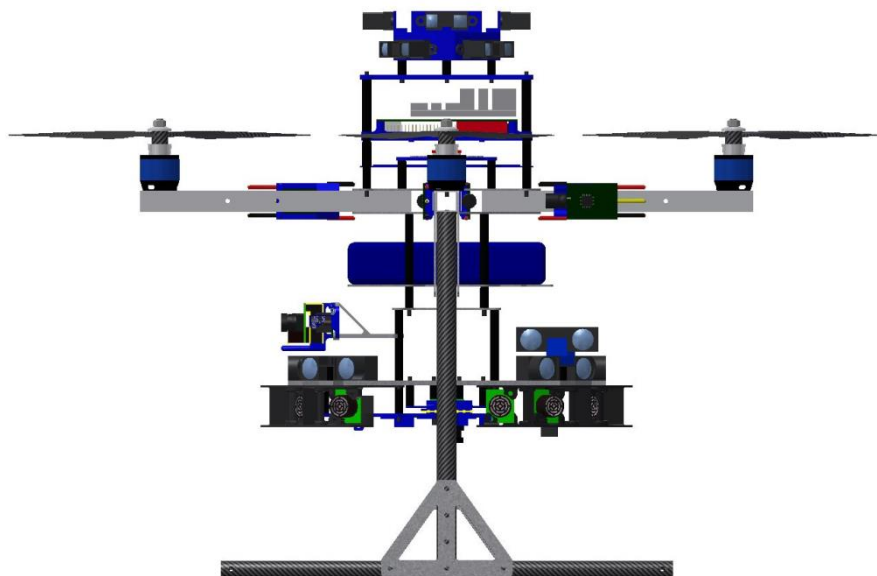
Seitenansicht des AQopterI8, CAD Design (CAD Zeichnung Sascha Dechend)
